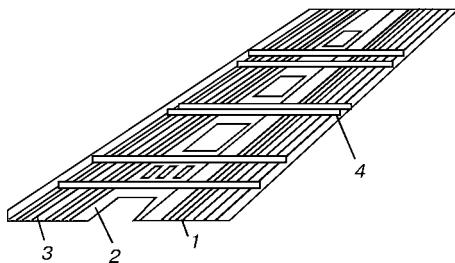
Элементы обшивки боковой стенки: 1 — семизигитовый гофрированный профильный лист, формирующий низ; 2 — обшивочный гофрированный лист, формирующий оконные проемы; 3 — трехзигитовый гофрированный профильный лист, формирующий верх; 4 — жесткая рама
